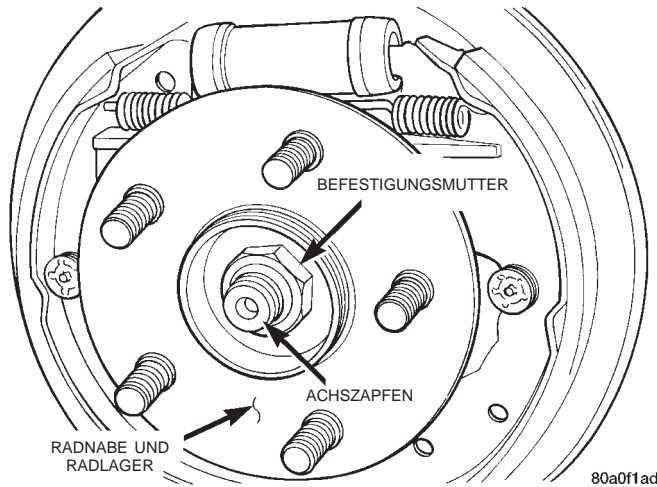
Befestigungsmutter für Radnabe und Radlager
